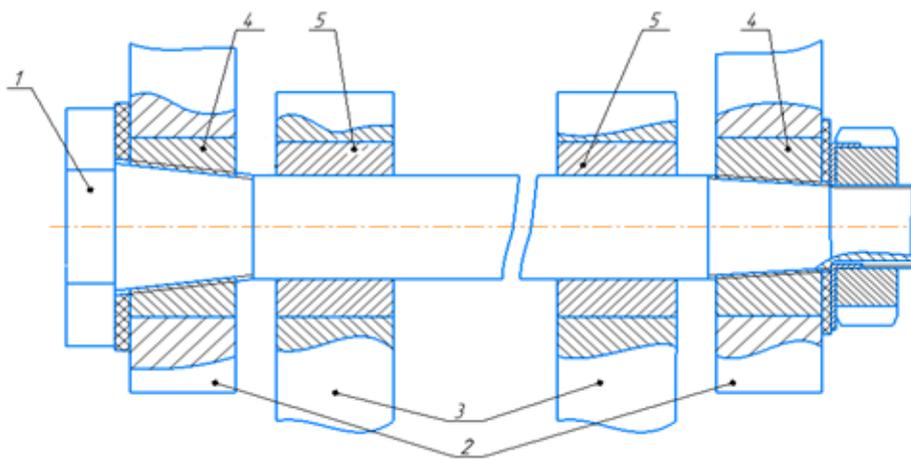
Конструкция шарнира с неподвижным резьбовым соединением: 1 - шарнирный палец с конической наружной резьбой; 2, 3 - проушины смежных элементов манипулятора; 4 - вкладыши с внутренней конической резьбой; 5 - вкладыши подшипников скольжения.
